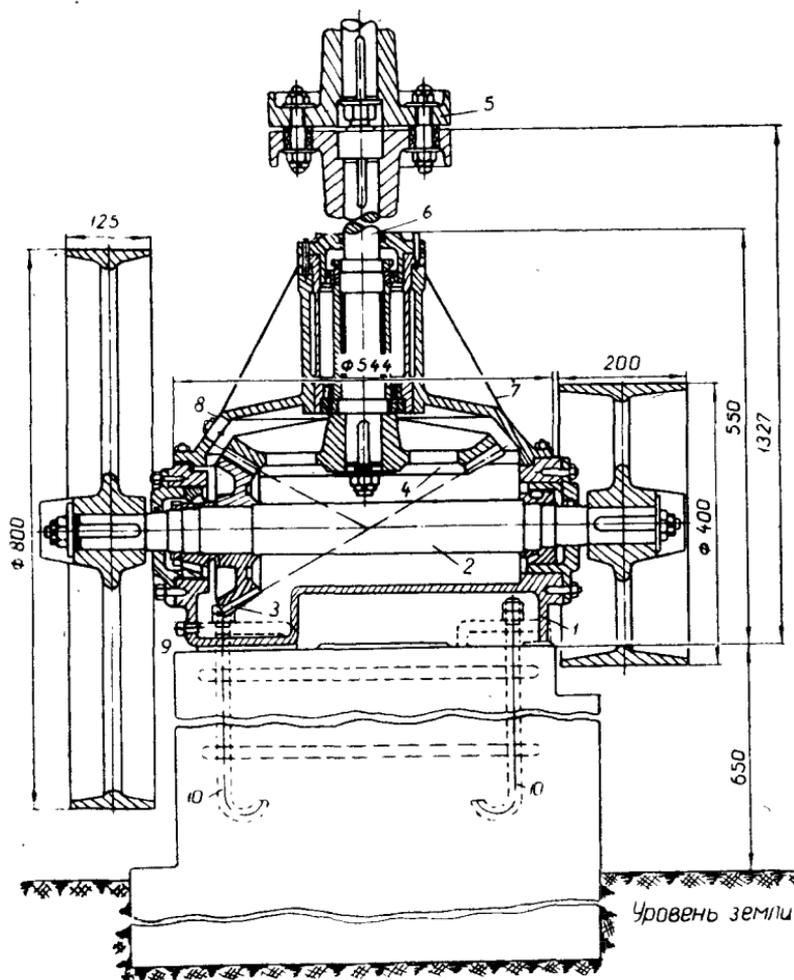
Нижний редуктор ветродвигателя Д-12:
